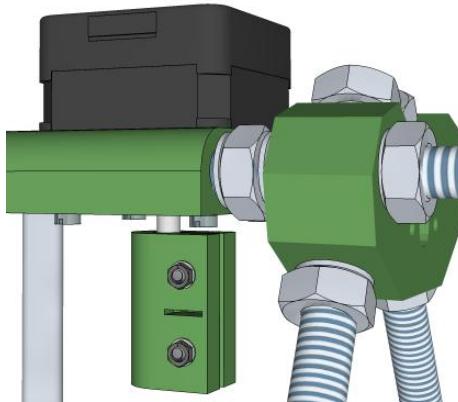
Preparación de extremos en X y ensamblado del eje Z (paso 13)
